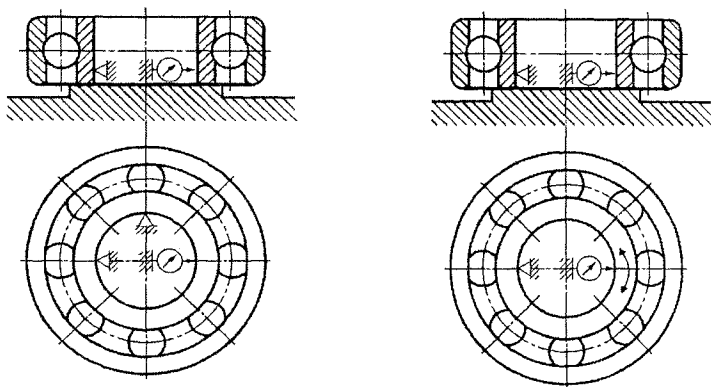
Схемы измерения отверстия внутреннего кольца подшипника
